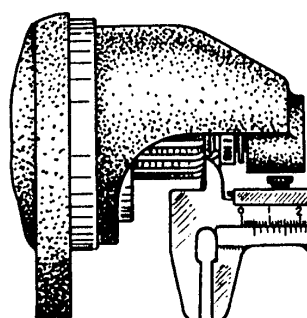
Замер зазора от торца шестерни до упорного кольца
